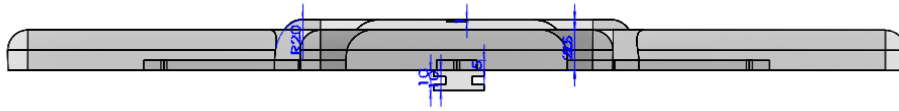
Vue latérale montrant la forme et les dimensions de la glissière.
